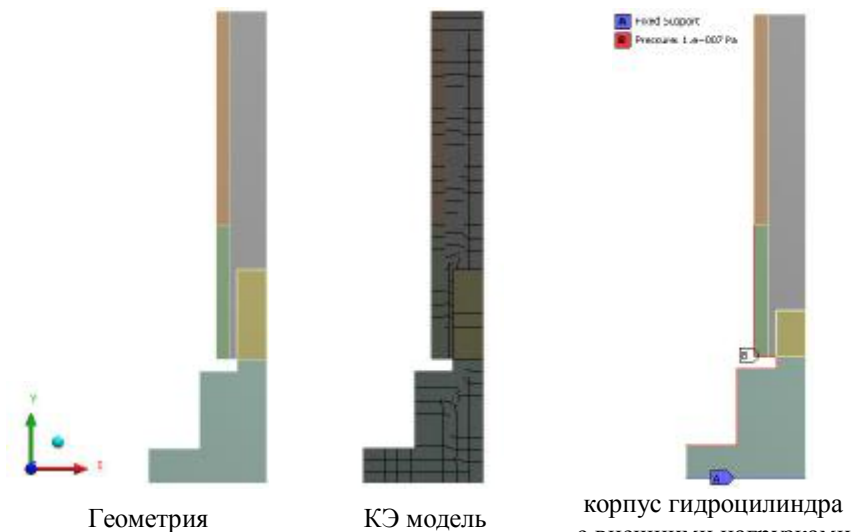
Геометрия и КЭ модель корпуса гидроцилиндра с внешними нагрузками
